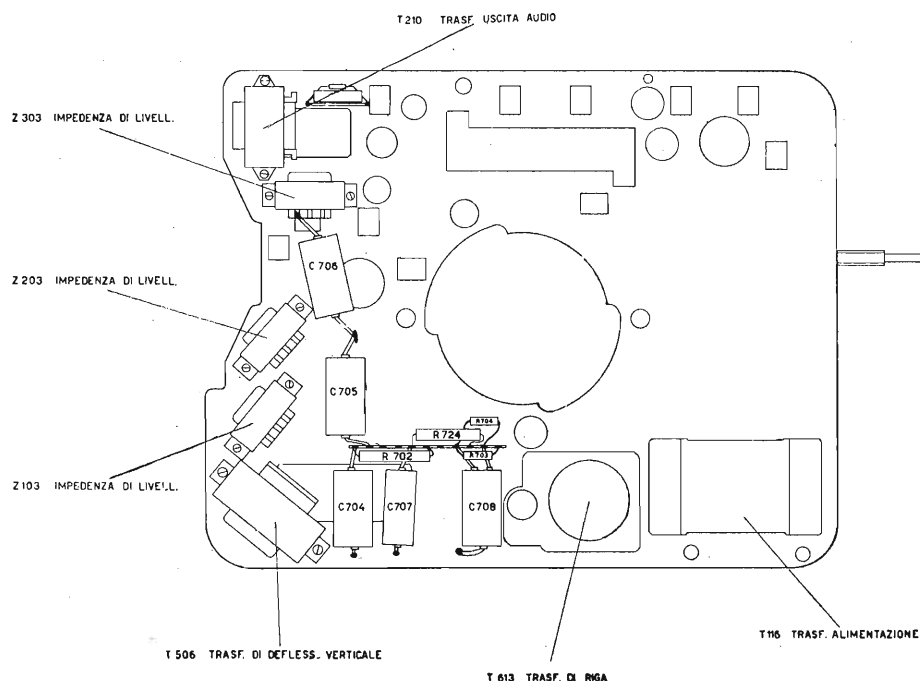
Disposizione dei componenti sulla parte inferiore dello chassis del televisore CM901.
